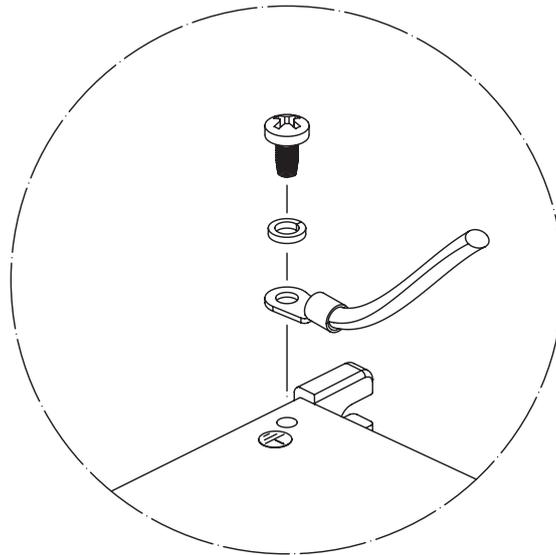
Dettaglio di montaggio collegamento di terra equipotenziale esterno
